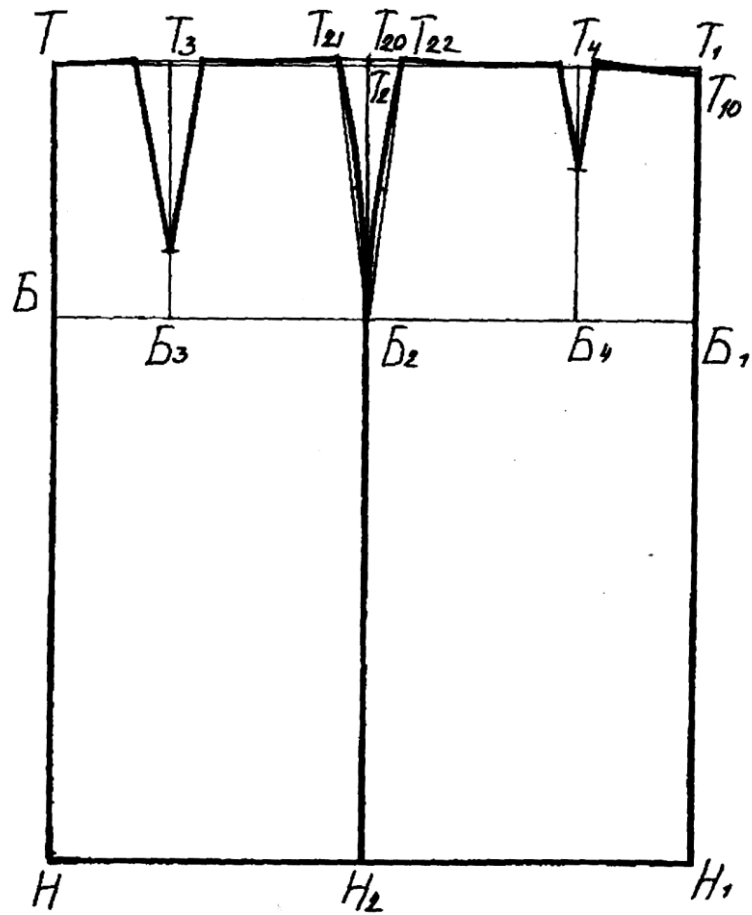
Чертеж конструкции прямой классической юбки с тремя вытачками
